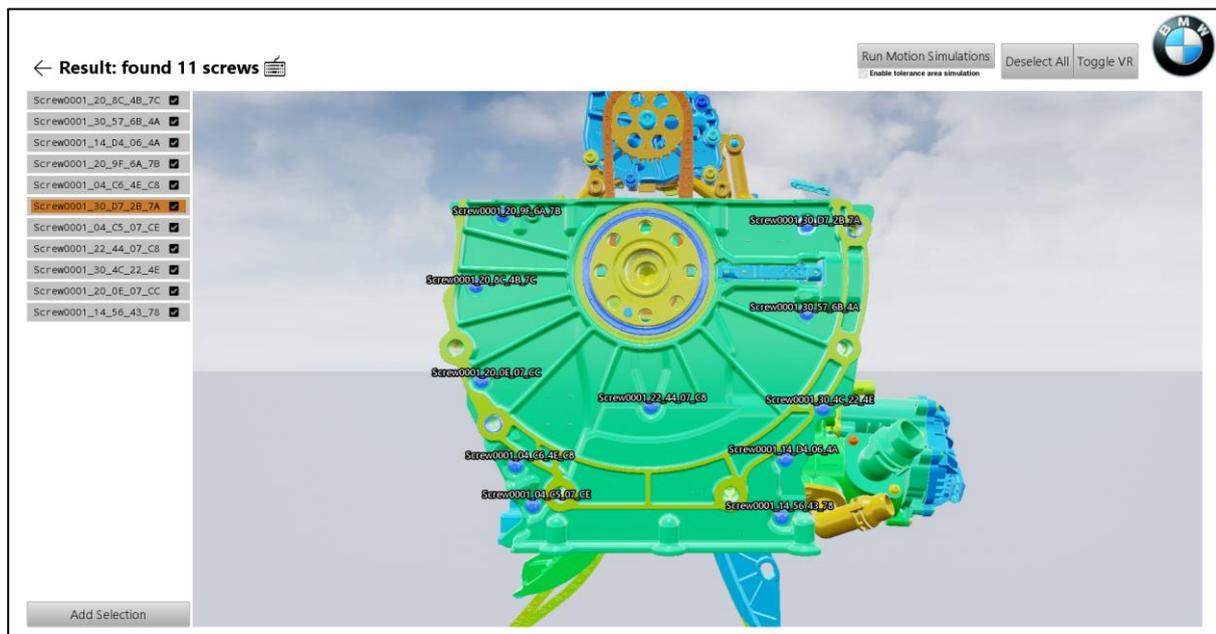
Gefundene Schrauben in dem AssemblyCheckTool
